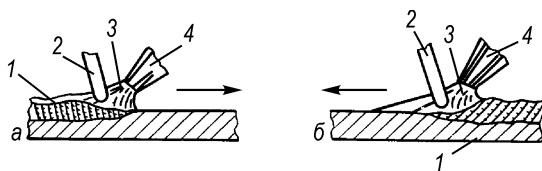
(а,б). Основные способы газовой сварки: 1 – формирующийся шов; 2 – присадочный пруток; 3 – пламя горелки; 4 – горелка
